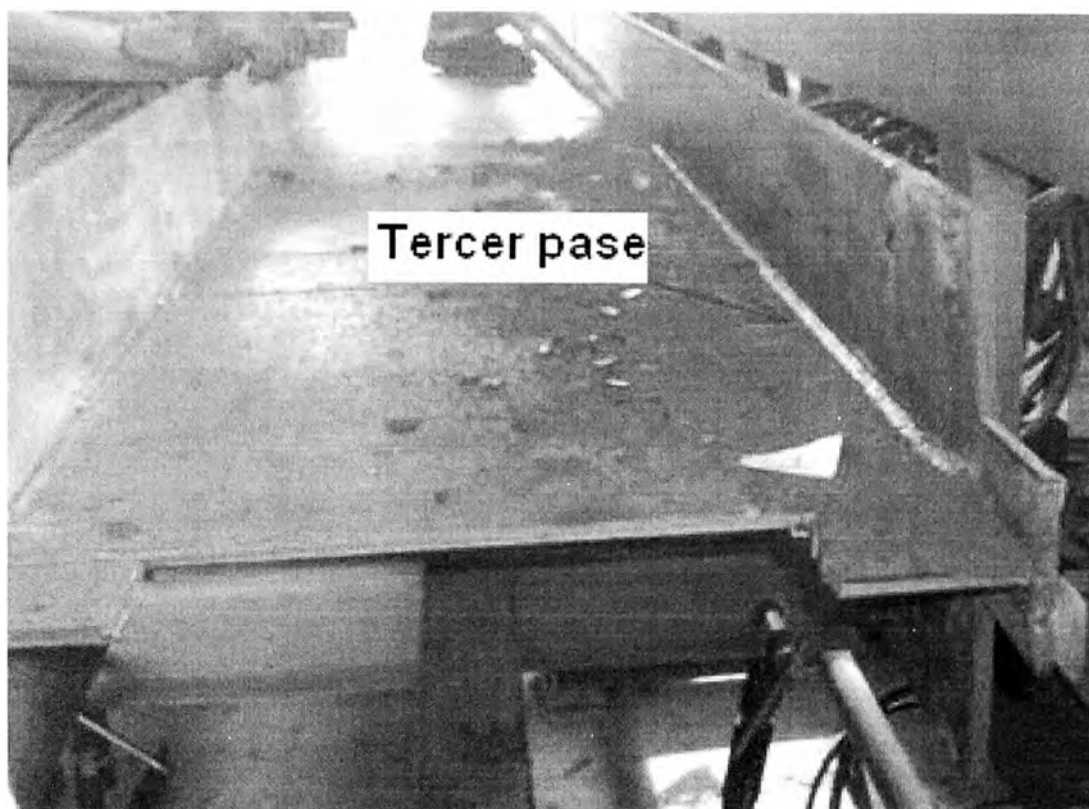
Soldadura del tercer cordón con SAW.
